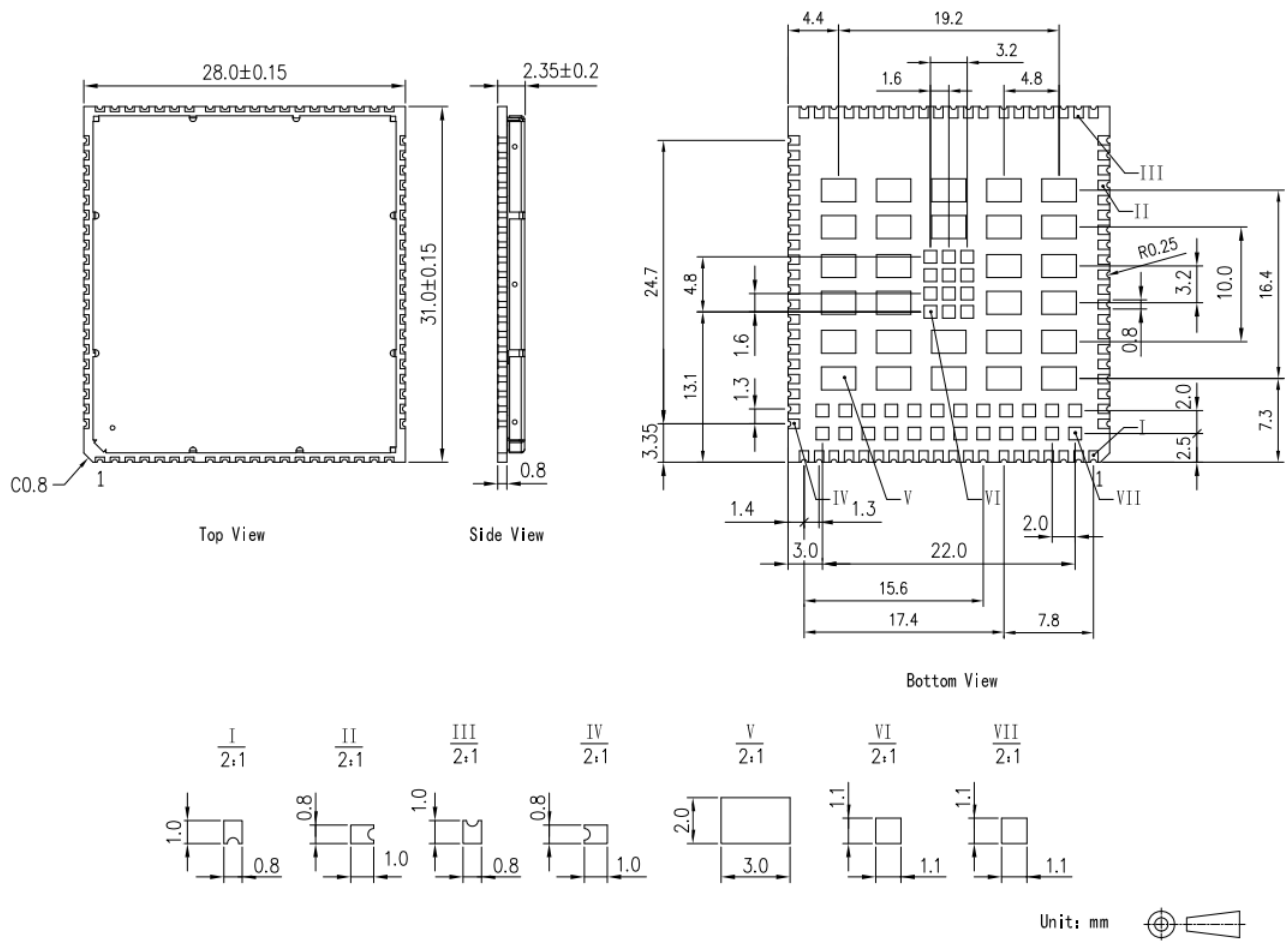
结构尺寸 TOP 视图、SIDE 视图和 BOTTOM 视图（单位：mm）
